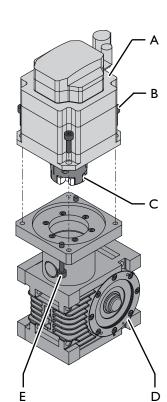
Motor entfernen: Getriebeeinheit Güdel
